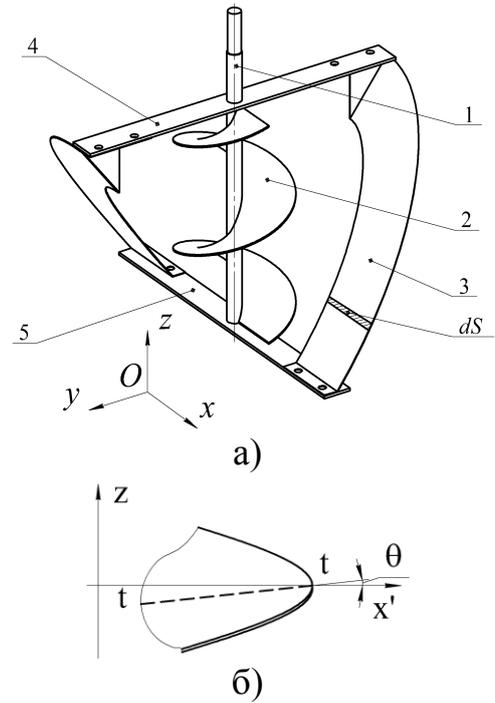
Робочий орган змішувача: а – вид аксонометрії; б – середня ділянка шнекової стрічки у вертикальній площині, що проходить через вісь z; 1 – вертикальний вал, 2 – внутрішній шнек з поверхнею гелікоїда, 3 – зовнішня шнекова стрічка зі змінною твірною, 4 – верхній кронштейн, 5 – нижній кронштейн, dS – елементарна ділянка стрічки шнека; t-t – твірна шнекової стрічки у вертикальній площині; θ – кут нахилу твірної
